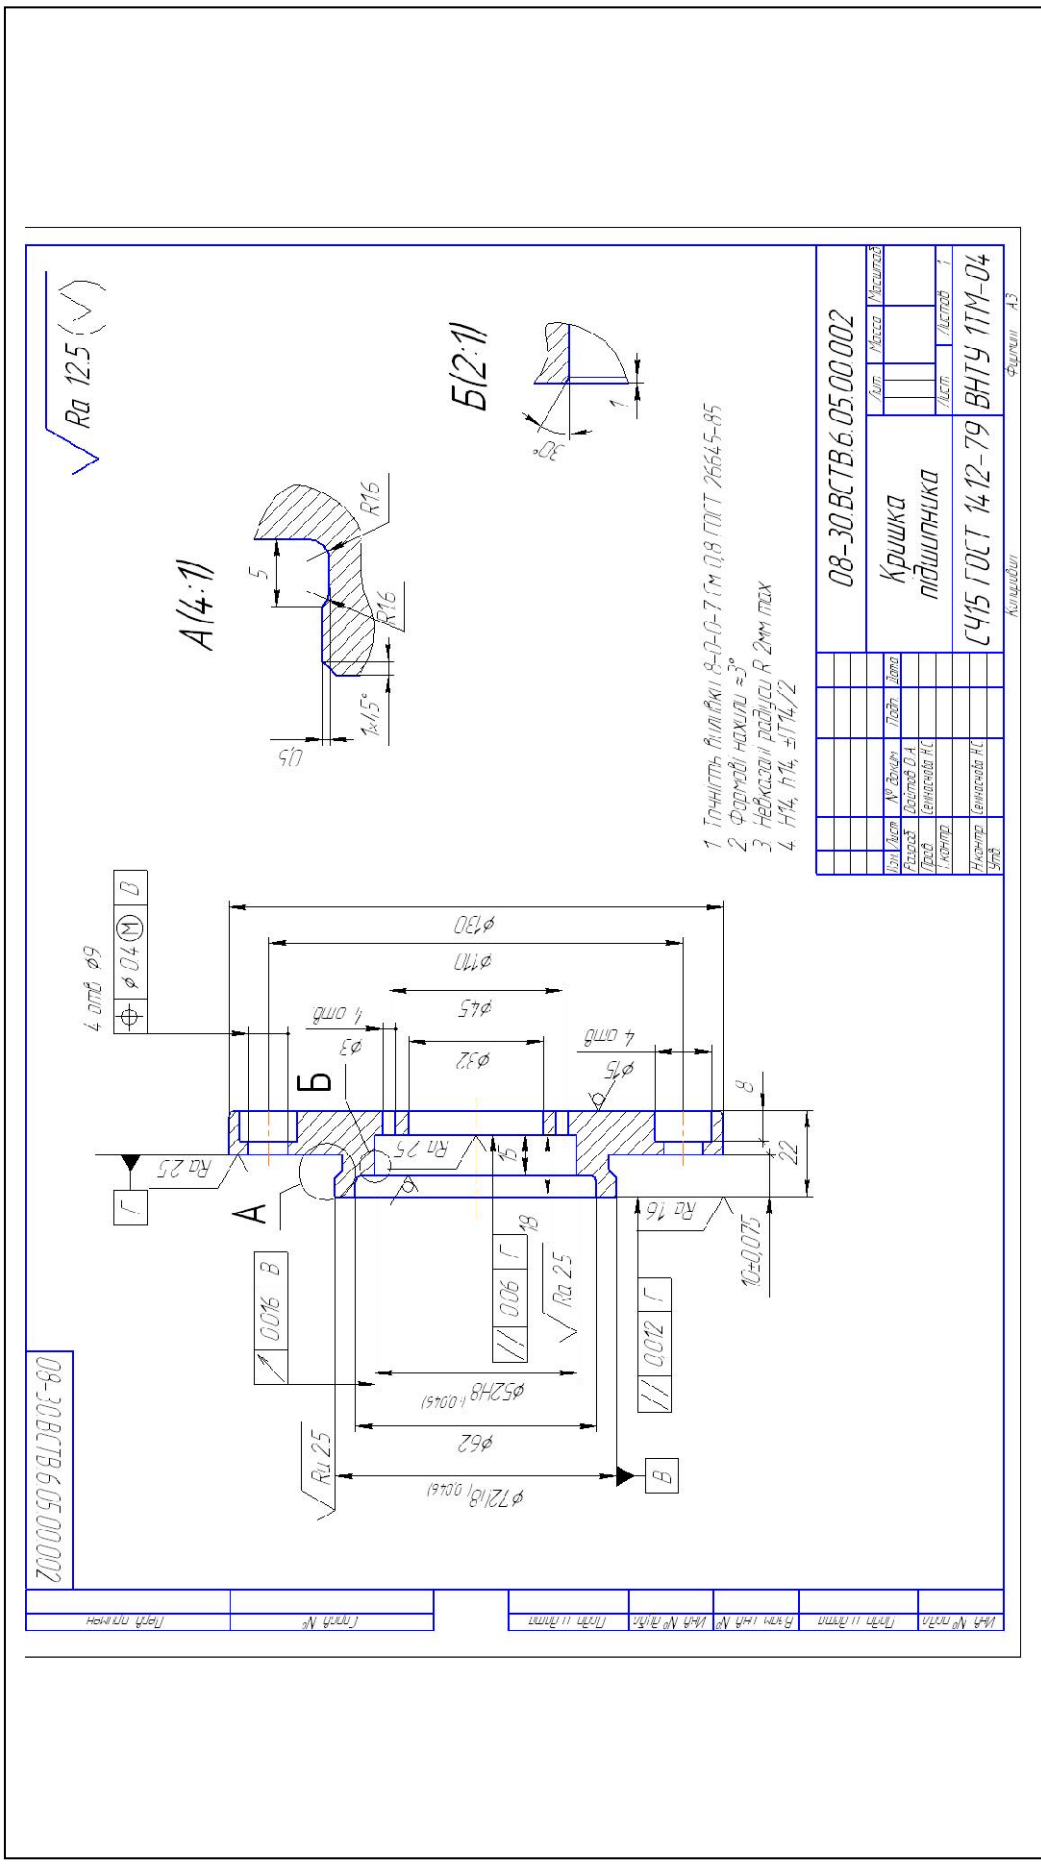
Приклад робочого креслення деталі «Кришка підшипника»
